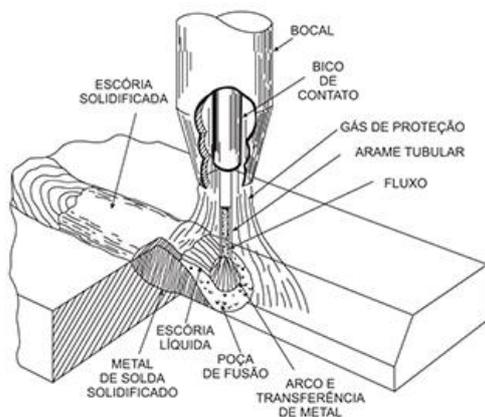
Processo de soldagem GMAW (MIG/MAG)
